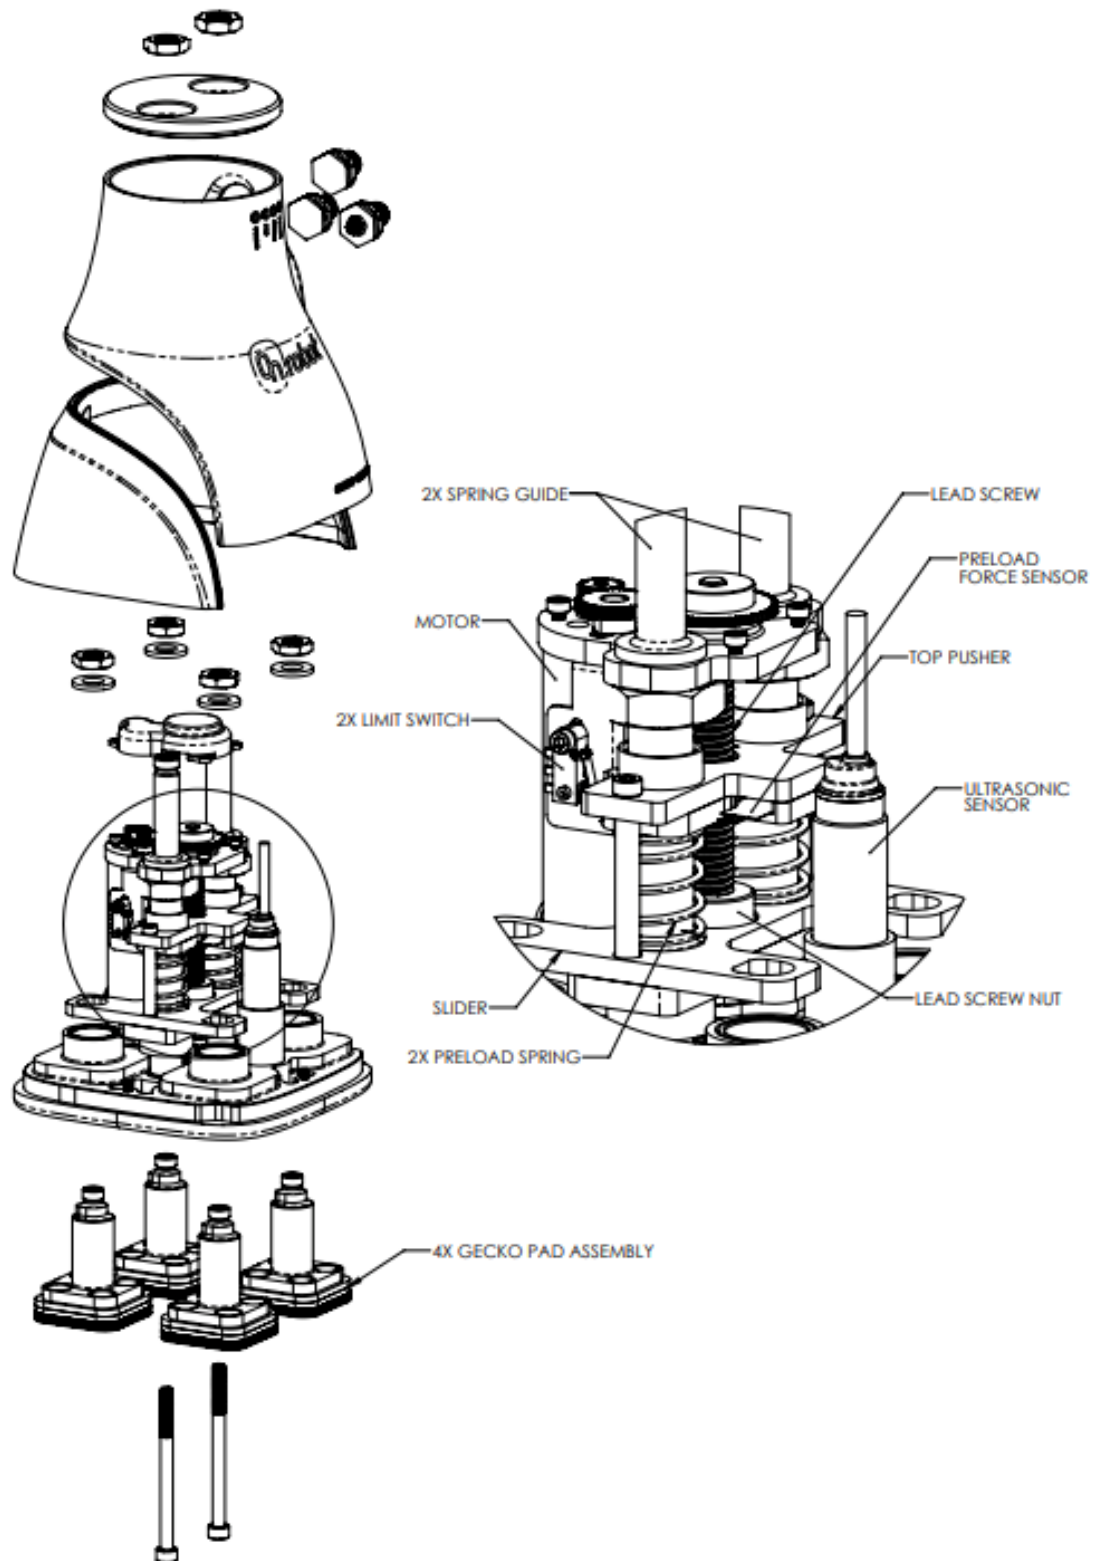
Dibujo de CAD de Gecko Gripper y las almohadillas.
